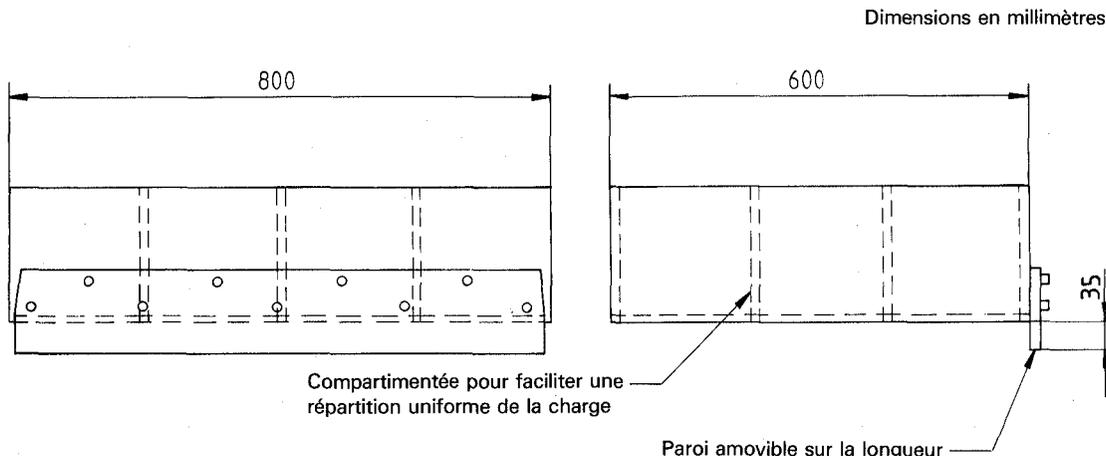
Caisse de chargement pour les essais sur plan incliné
